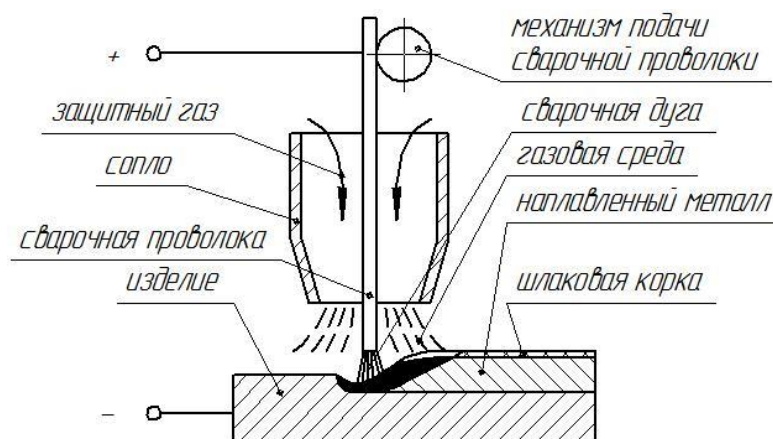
Схема осуществления сварки в среде защитных газов
